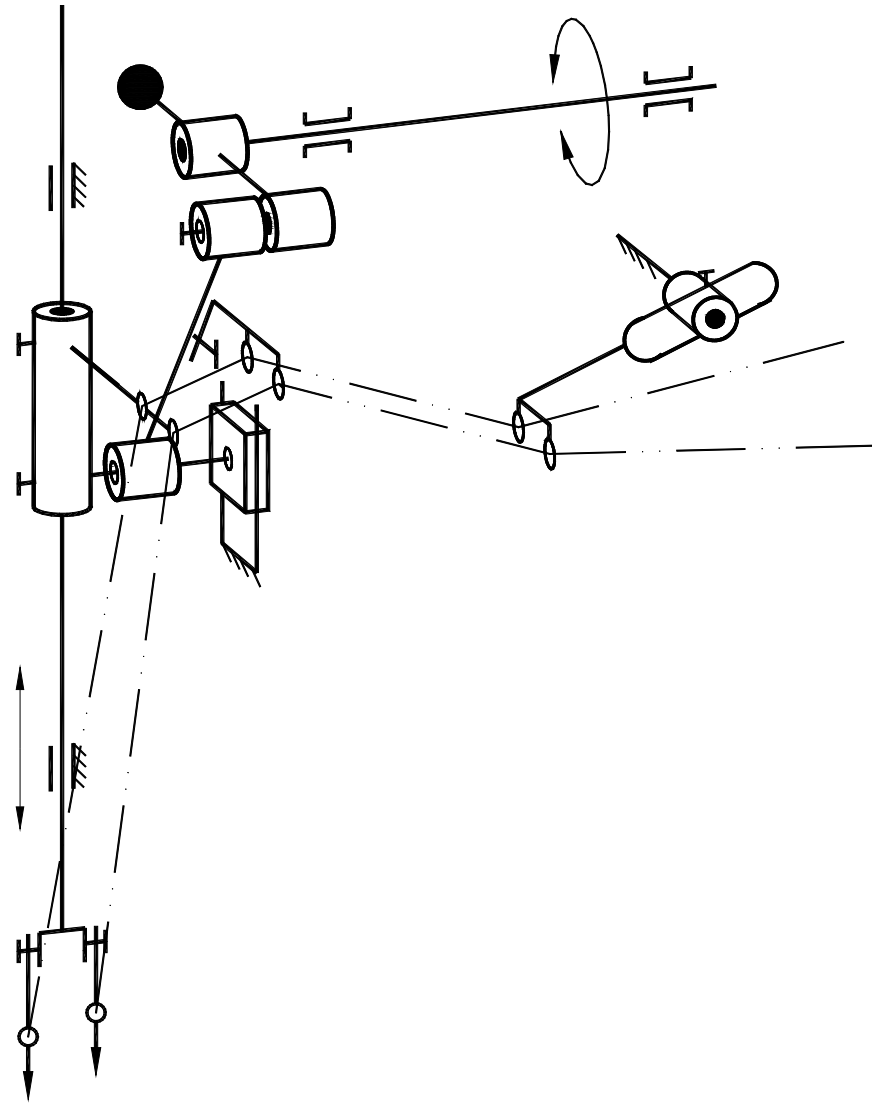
Механізм подачі нитки ш.м. 876 ПМЗ
